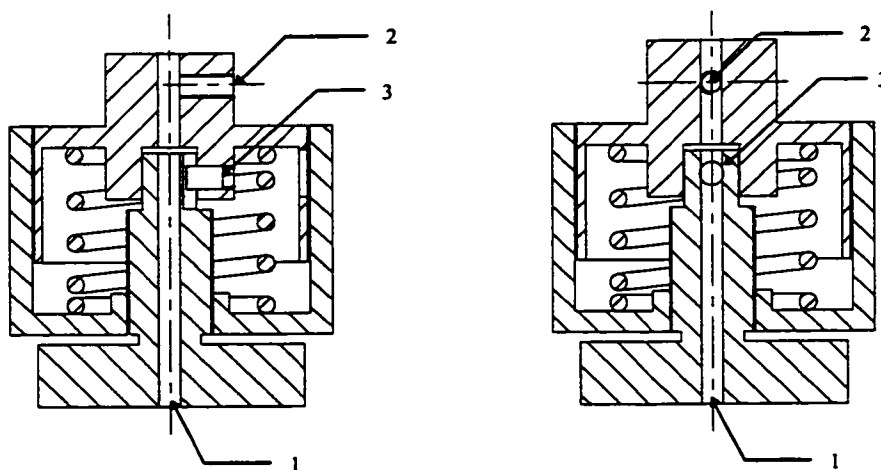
Dessin d'assemblage du dispositif de mise en charge.
